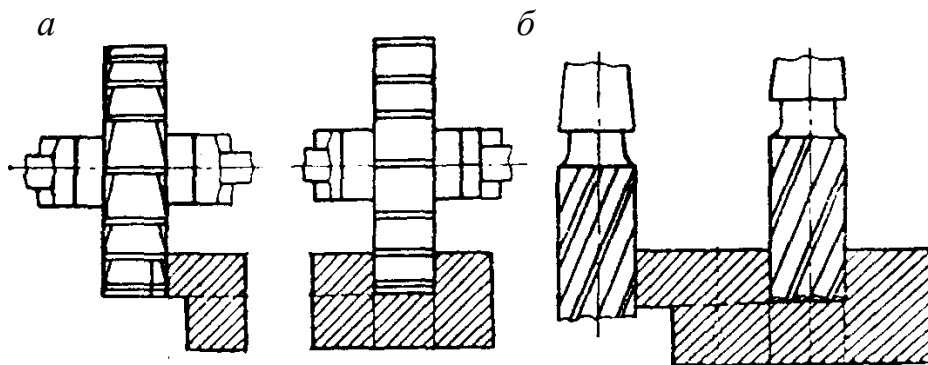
Пример цилиндрического и торцевого фрезерования
